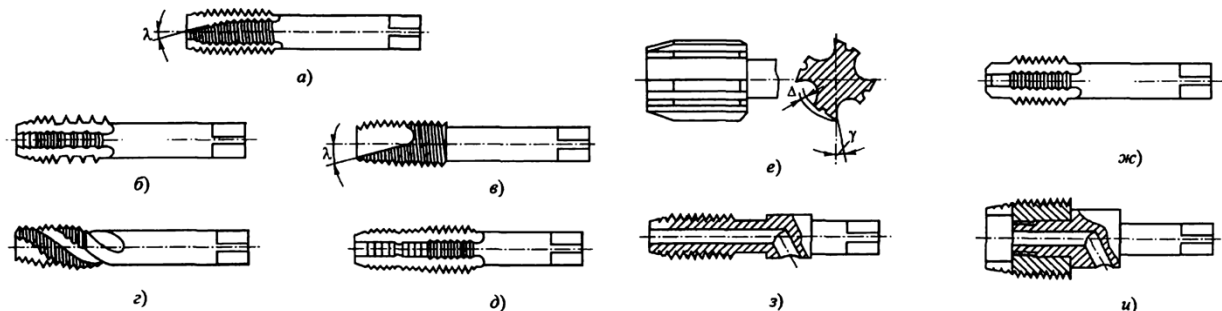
Конструкции отдельных типов метчиков: а – ручной; б – с шахматным расположением зубьев; в – безканавочный; г – с винтовыми канавками; д – ступенчатый; е – с режуще-выглаживающими зубцами, ж – с направляющей частью; з – с внутренним подводом охлаждающей жидкости; и – колокольного типа
